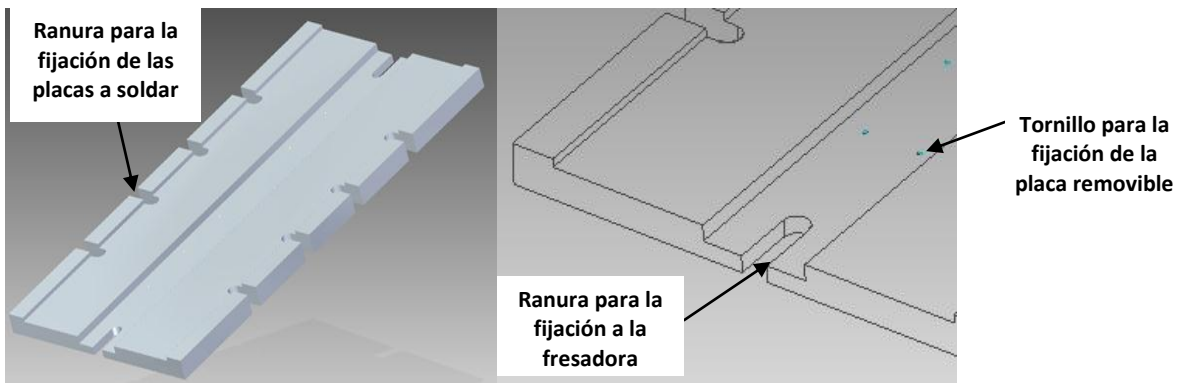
Placa de apoyo para la soldadura y protección de la fresadora diseñados mediante Solid Edge® ST5. Fuente propia.
